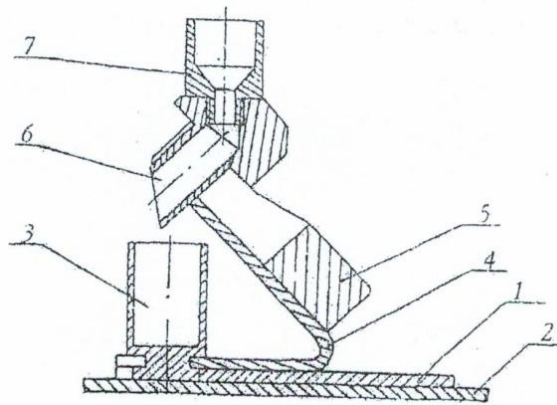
Устройство ферромагнитного сепаратора: 1 – направляющая; 2 – основание; 3 – стакан; 4 – кронштейн; 5 – магнит; 6 – патрубок; 7 – емкость наливная
